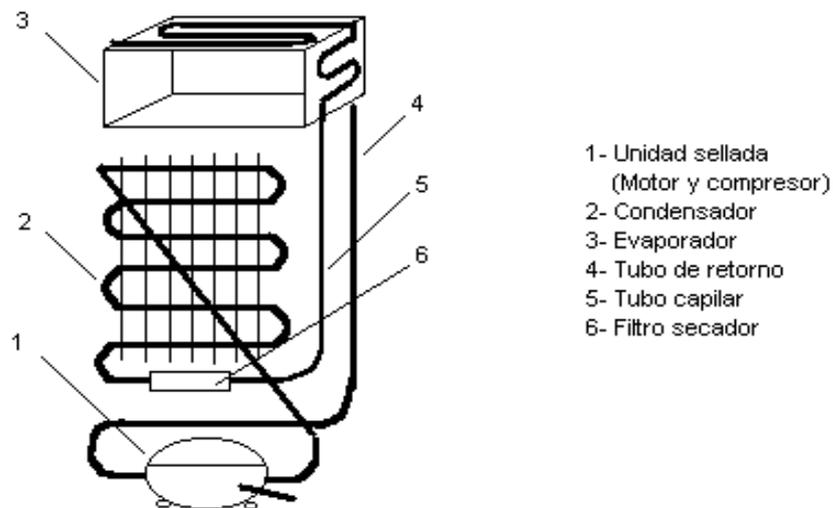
Partes principales de un sistema de refrigeración por compresión
